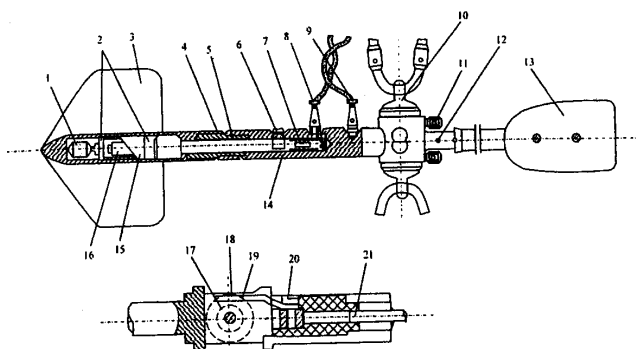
Устройство гидрометрической вертушки ГР-21М:
